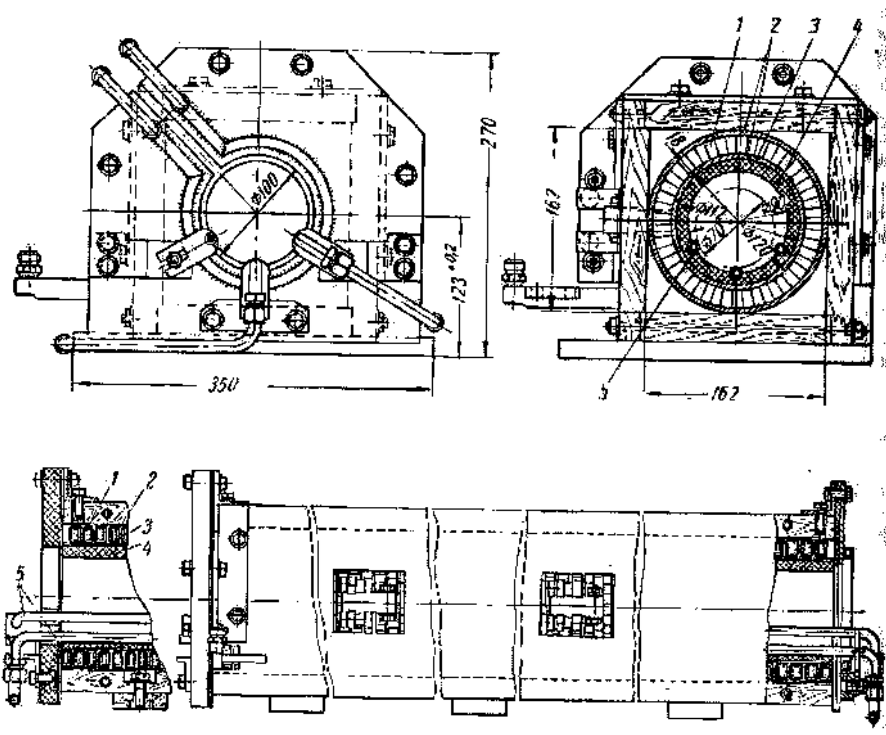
Індуктор для нагрівання циліндричних заготовок.
